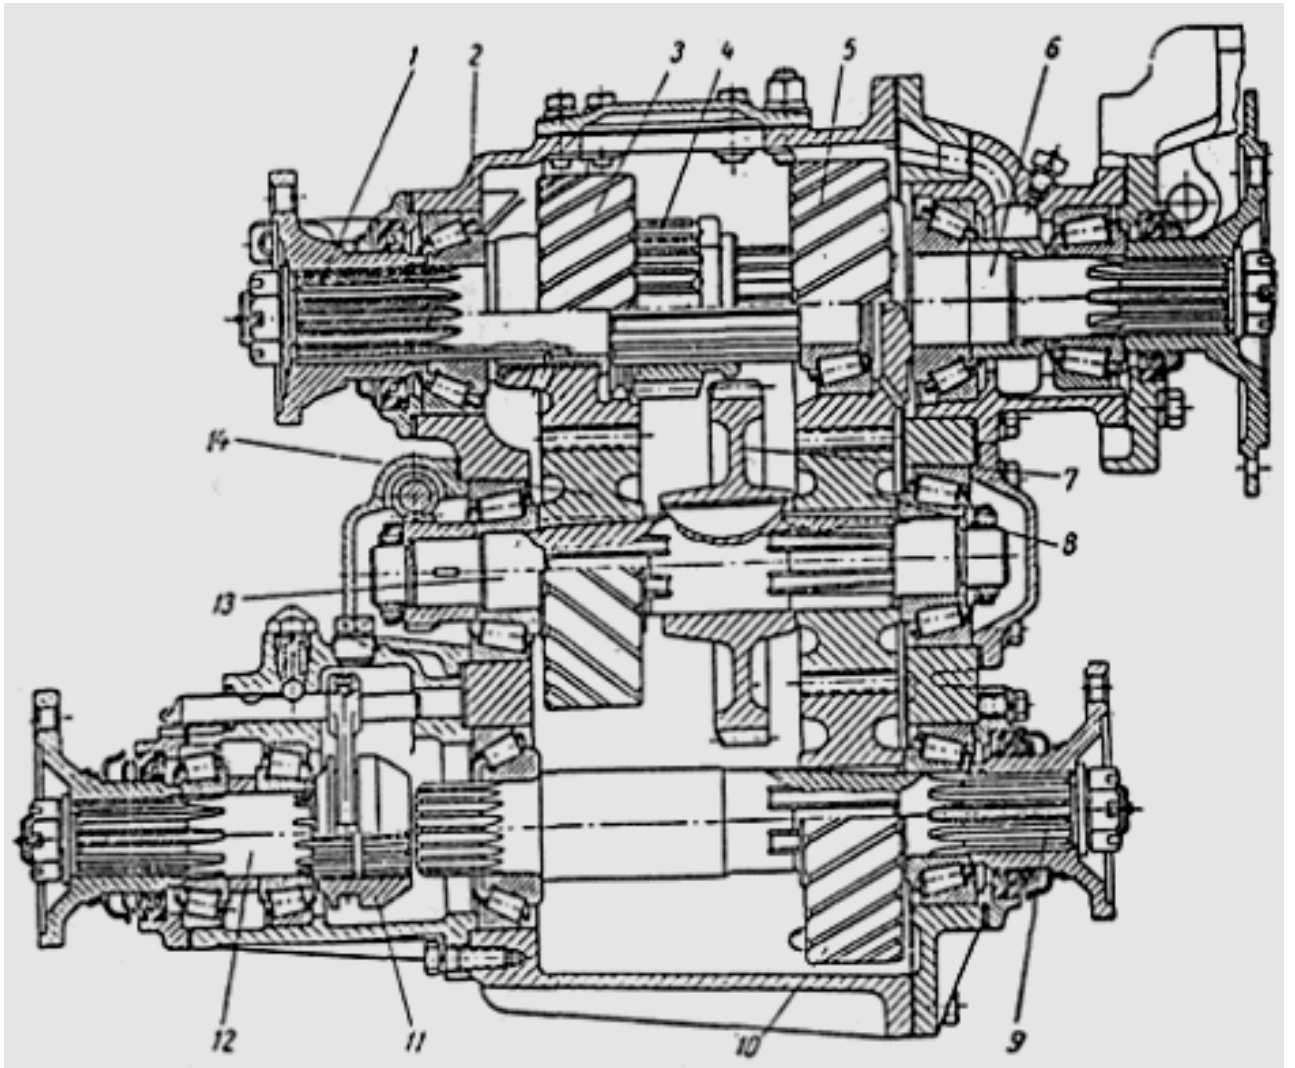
Раздаточная коробка 3-х-осного полноприводного автомобиля: 1 - ведущий вал; 2 - корпус; 3 - шестерня; 4 - передвижная шестерня; 5 - ведомая шестерня второго заднего моста; 6 - вал привода второго заднего моста; 7, 8, 14 - шестерни промежуточного вала; 9 - вал привода первого заднего моста; 10 - шестерня привода вала переднего и первого заднего мостов; 11 - муфта включения переднего моста; 12 - вал привода переднего моста; 13 - промежуточный вал; 14 - шестерня привода промежуточного вала
